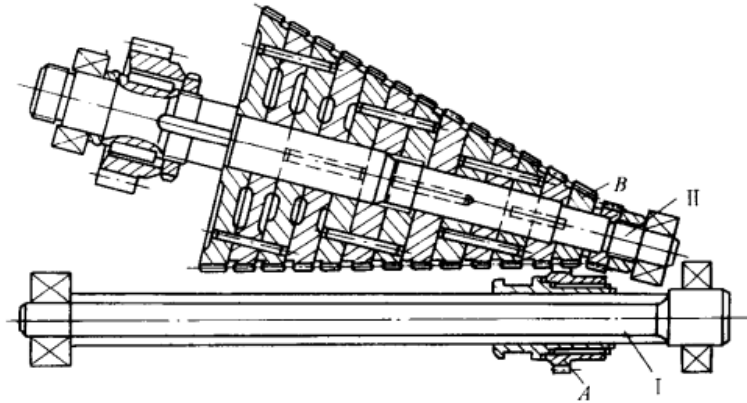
单齿轮滑移锥齿轮组多级变速机构
